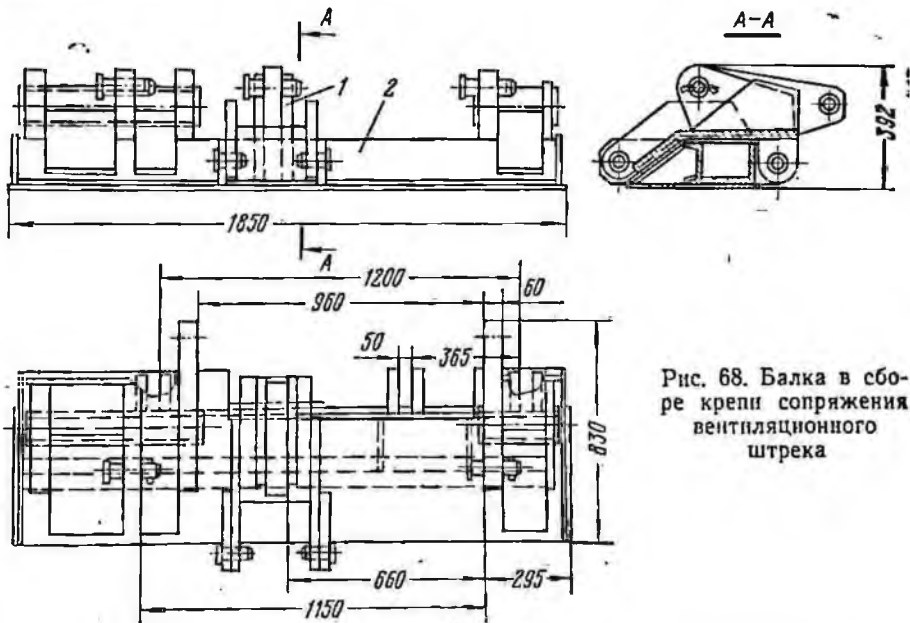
Балка в сборе крепя сопряжения вентиляционного штрека
